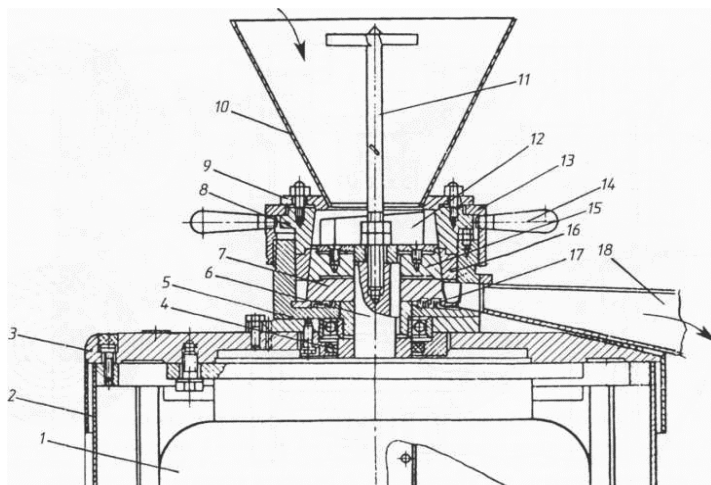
Режущий механизм эмульсатора К6-ФКМ:
